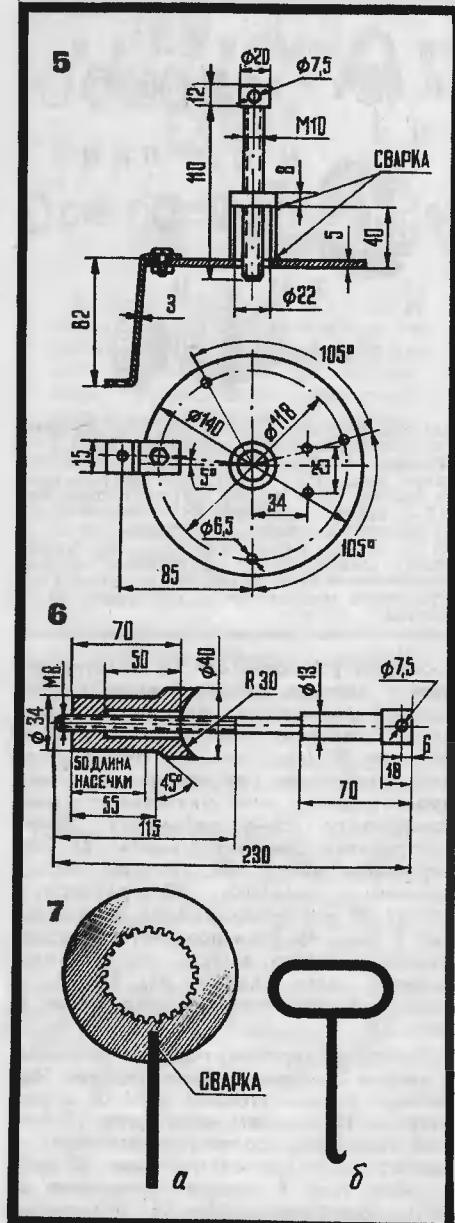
Приспособление для разъединения половинок картера и извлечения коленчатого вала.
